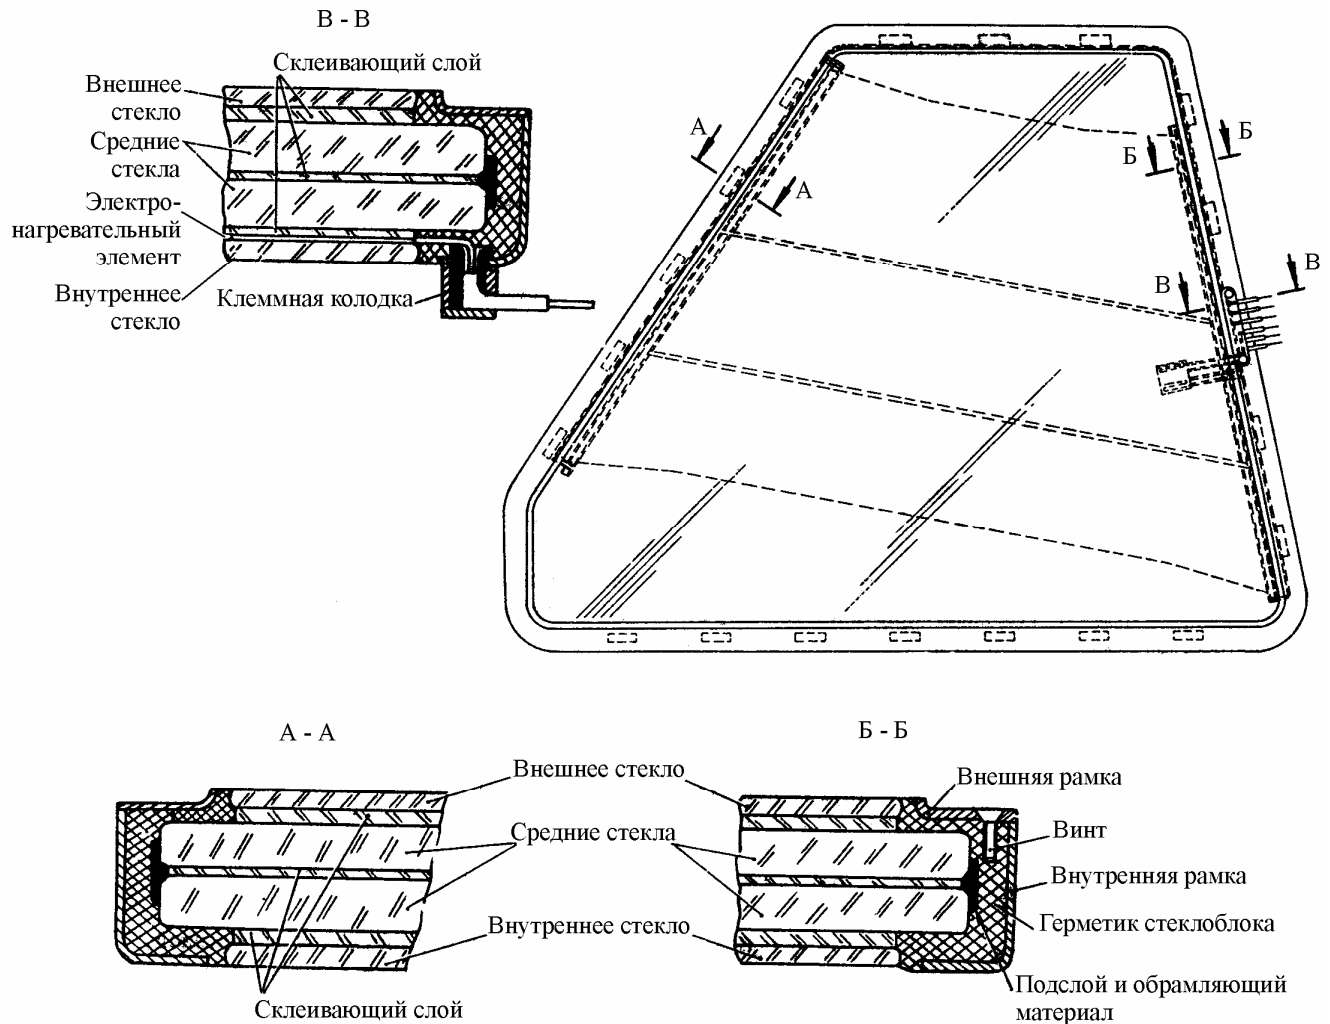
Стеклоблок форточка (вид изнутри на правый борт)
